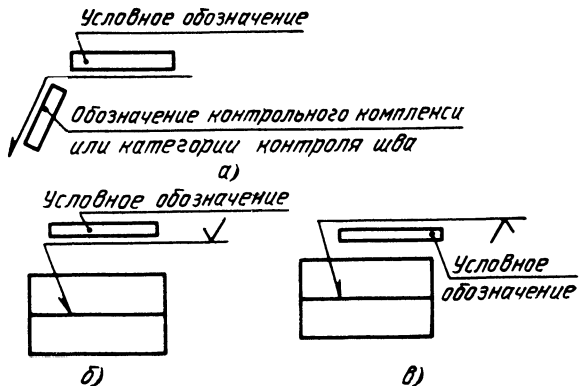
Нанесение условных обозначений и шероховатости обработанной поверхности:
